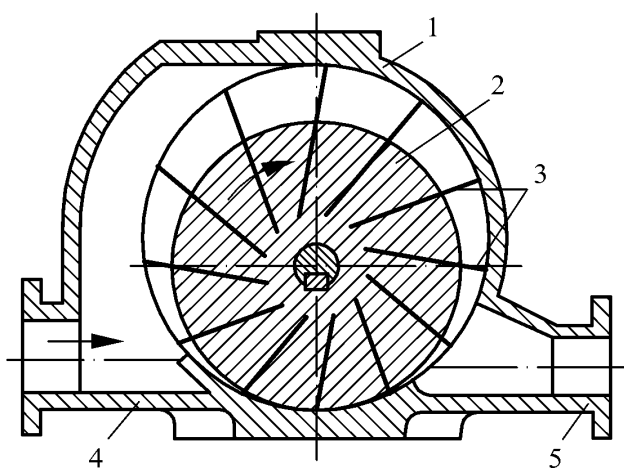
Конструктивная схема роторного компрессора: 1 – корпус; 2 – ротор; 3 – пластины; 4 – всасывающий; 5 – подающий патрубок
